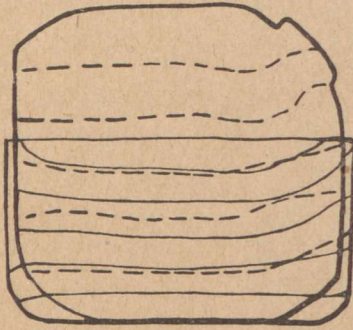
Schweißlinien einer Flacheisen-
